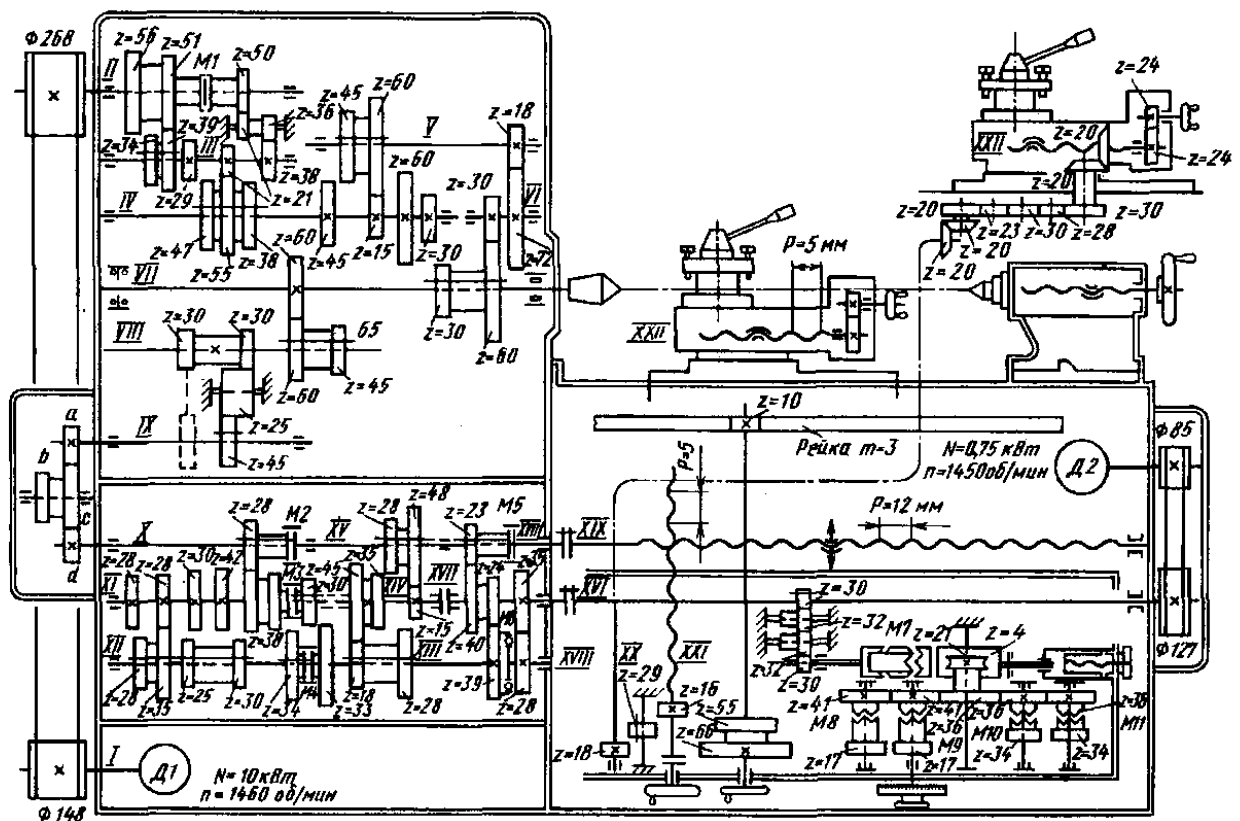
Кінематична схема токарного верстат 16K20
